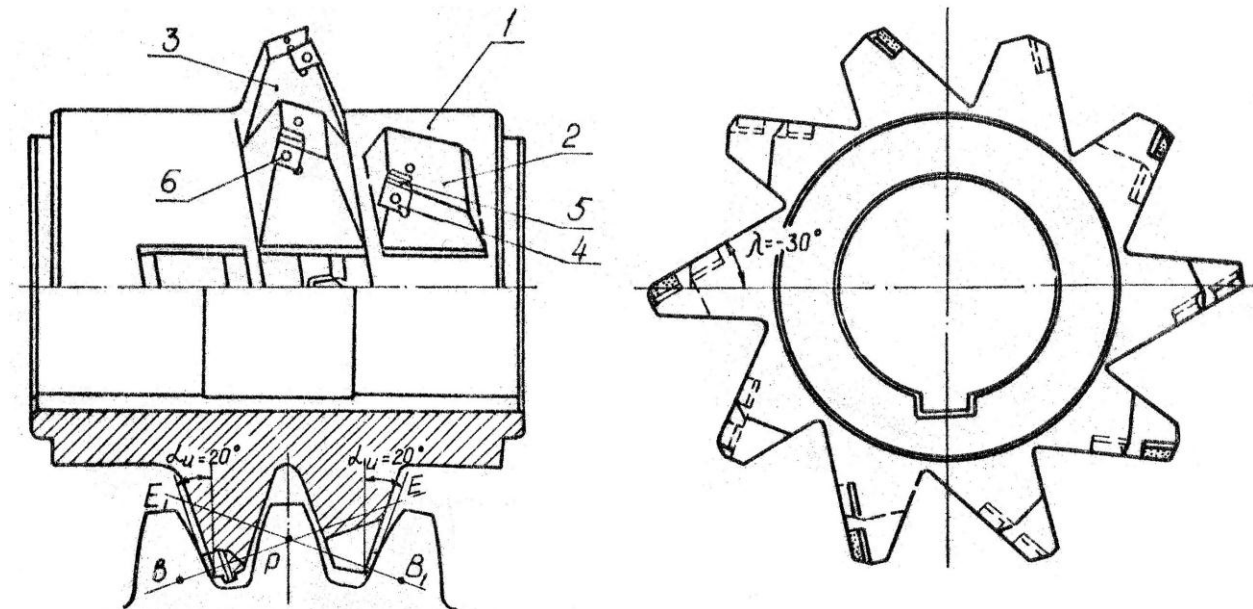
Червячная фреза с коническими зубчатыми выступами
